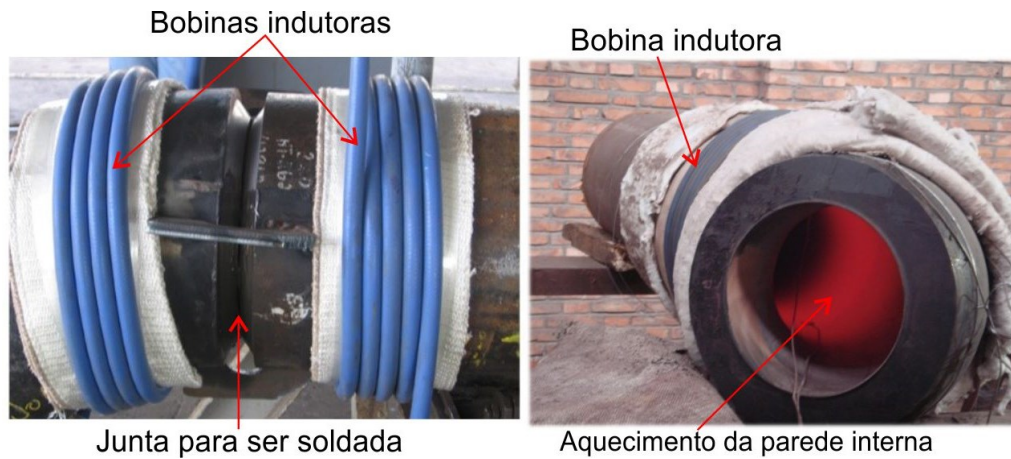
Montagem de bobinas de cabos para aquecimento por indução.
